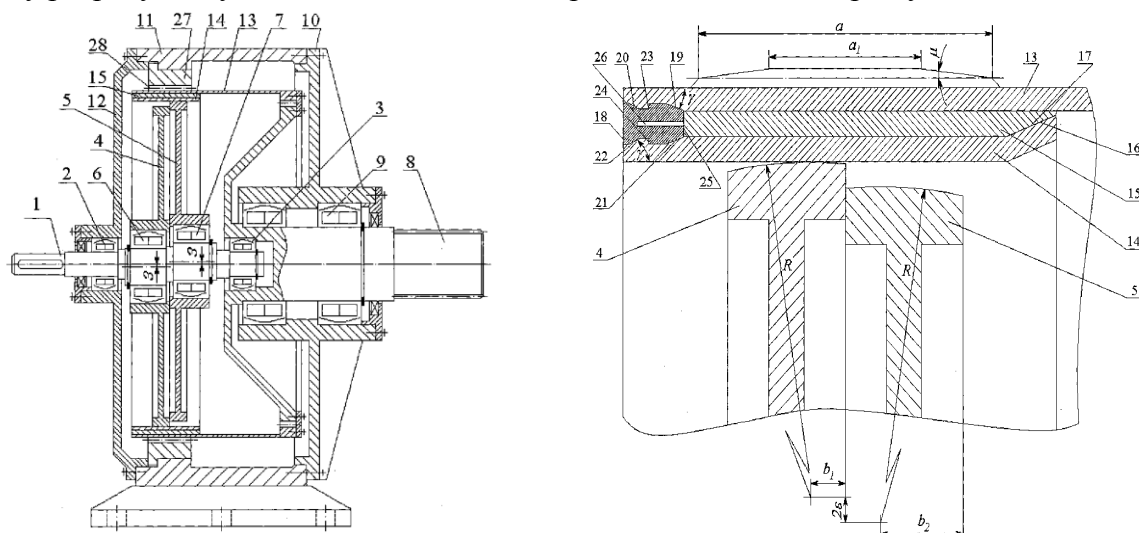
Розроблений великогабаритний хвильовий редуктор:
